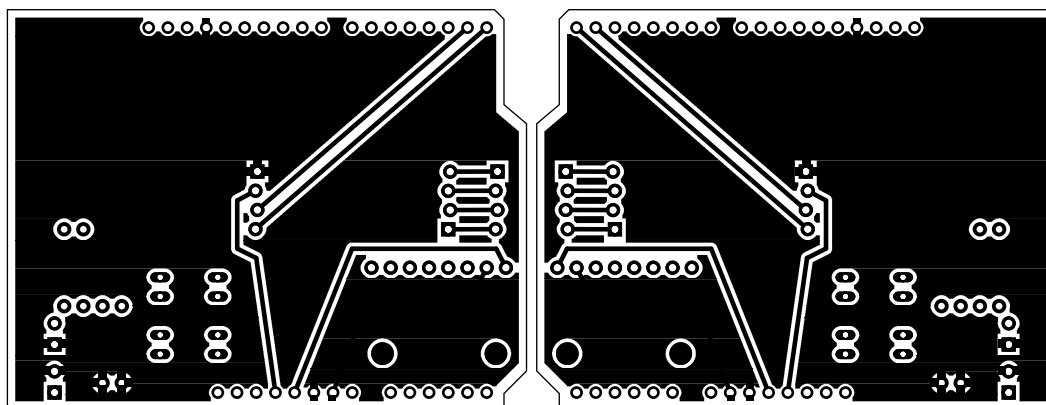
Circuito impresso da placa *Proteo Shield* em tamanho real. Parte superior.
